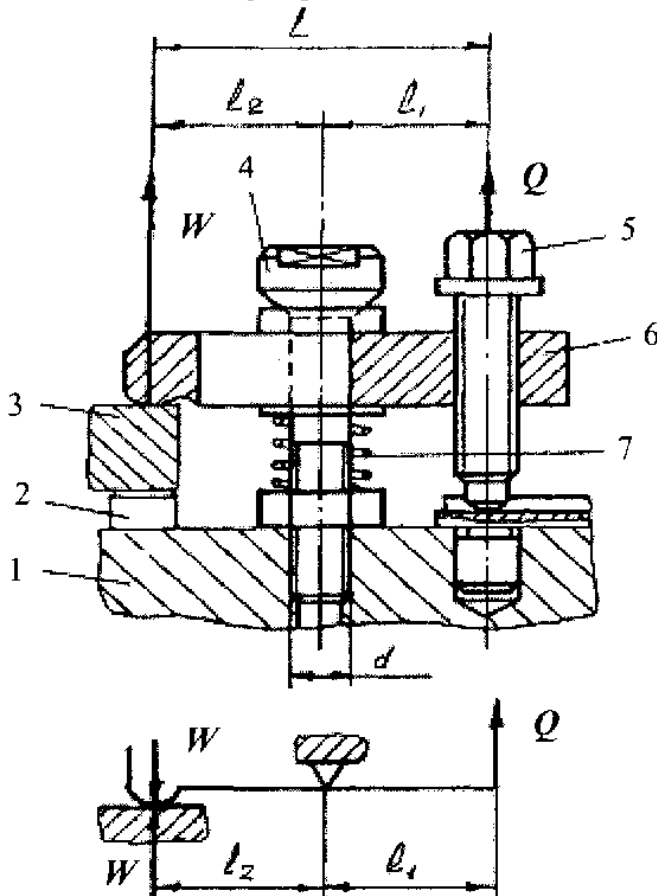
Схема нормалізованого гвинтового прихвата
